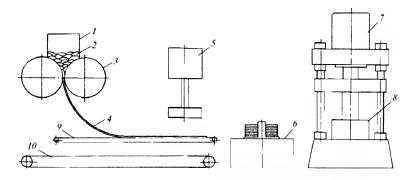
Поточно-механизированная линия с одноклетевым станом дуо: 1— загру зочный бункер; 2— кусковая абразивная масса; 3— клеть дуо; 4— полуфабрикат листа; 5— вырубной пресс; 6— участок сборки пакетов; 7— гидравлическии пресс; 8— пресс-форма; 9— приемный гранспортер; 10— транспортер возврата облоя
